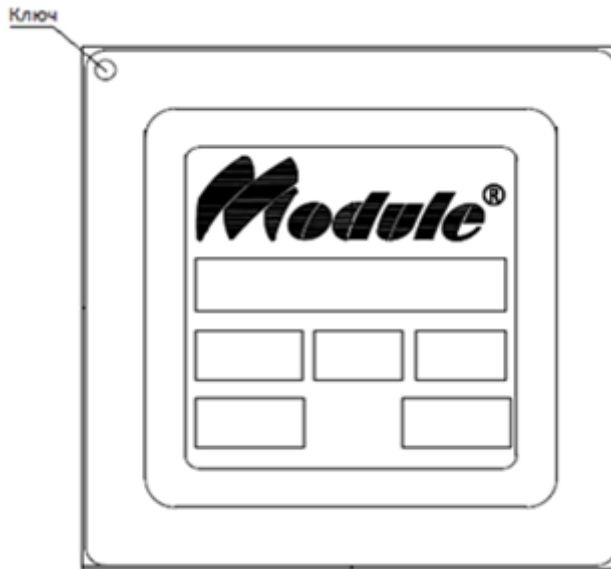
Корпус СБИС МИ БИУС, вид со стороны крышки корпуса
